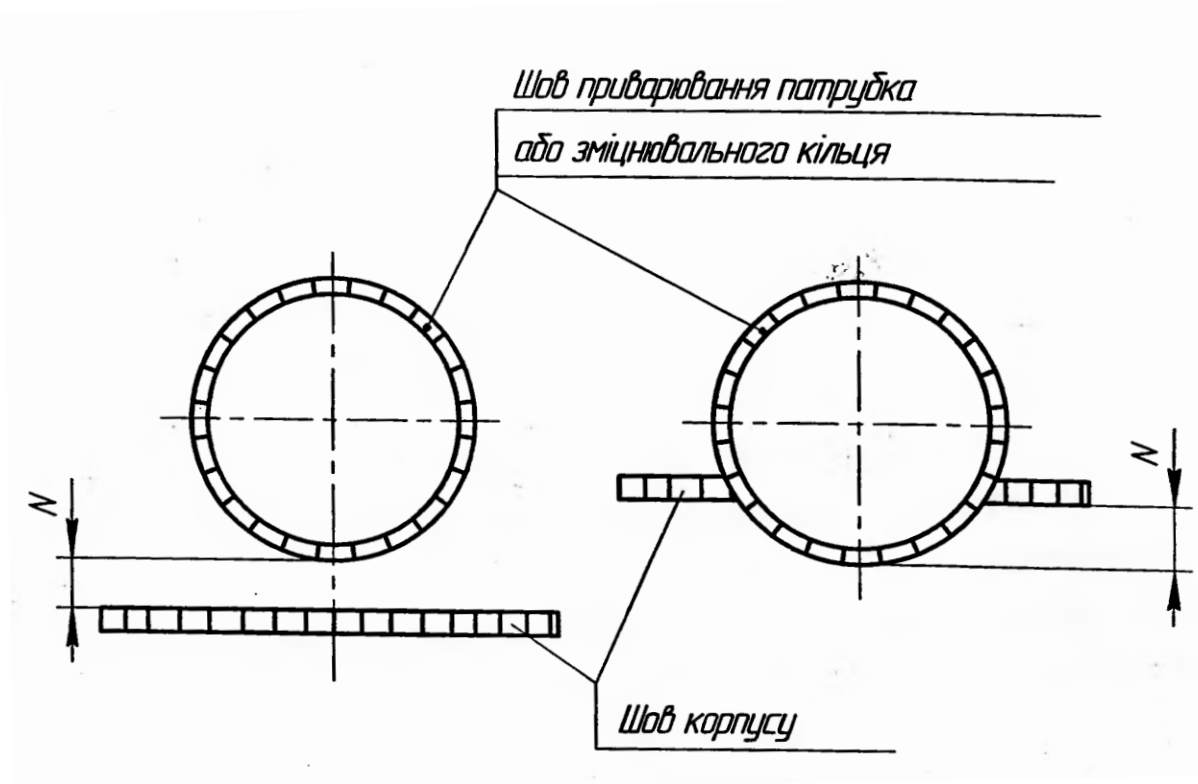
Схема визначення відстані між краєм шва корпусу та краєм шва приварювання деталі
